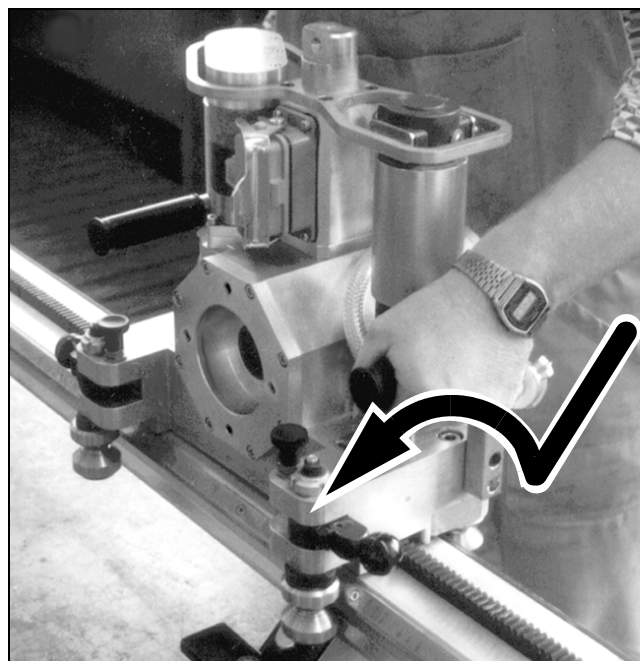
Установка корпуса пилы на направляющий рельс
